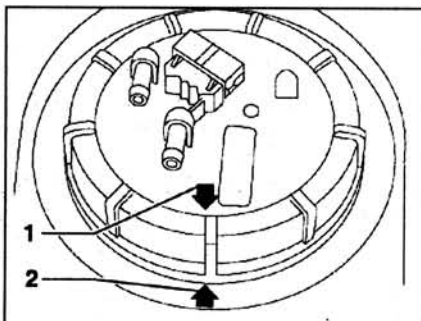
Топливный фильтр двигателей 2.8 CDI:
